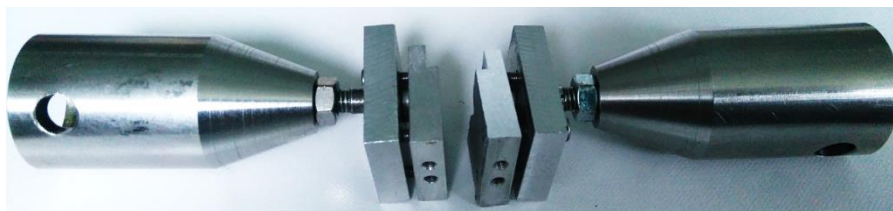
Système d'attache des éprouvettes de la figure 2.19 à la machine d'essai
